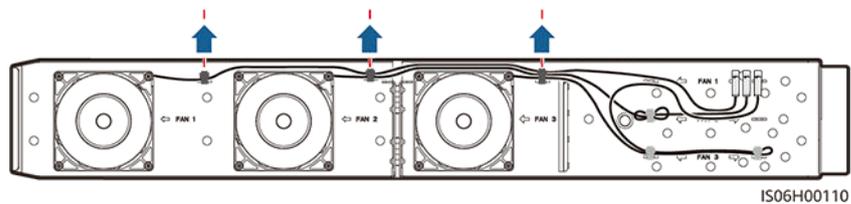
Extracción de la bandeja de ventiladores (2)
